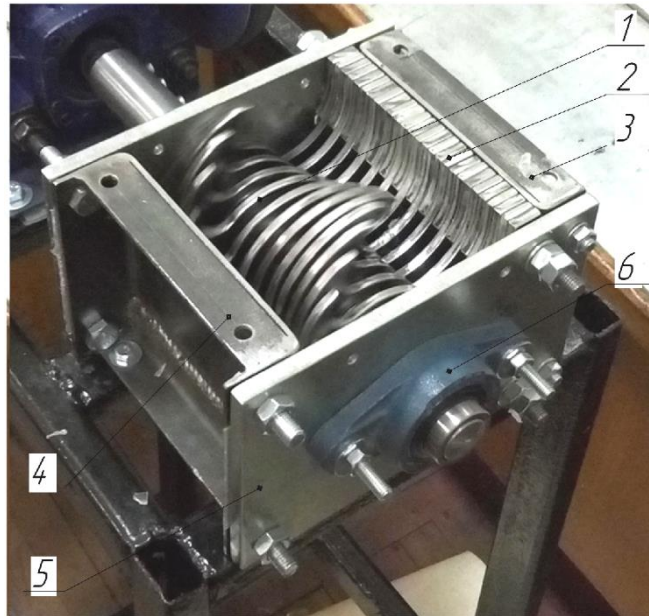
Конструкція шредера: 1 – вал з ножами; 2 – блок контр-ножів; 3, 4 – бічні стінки; 5 – опорні плити; 6 – опори валу з радіальними самоорієнтовними корпусними підшипниками марки UCFL205.
